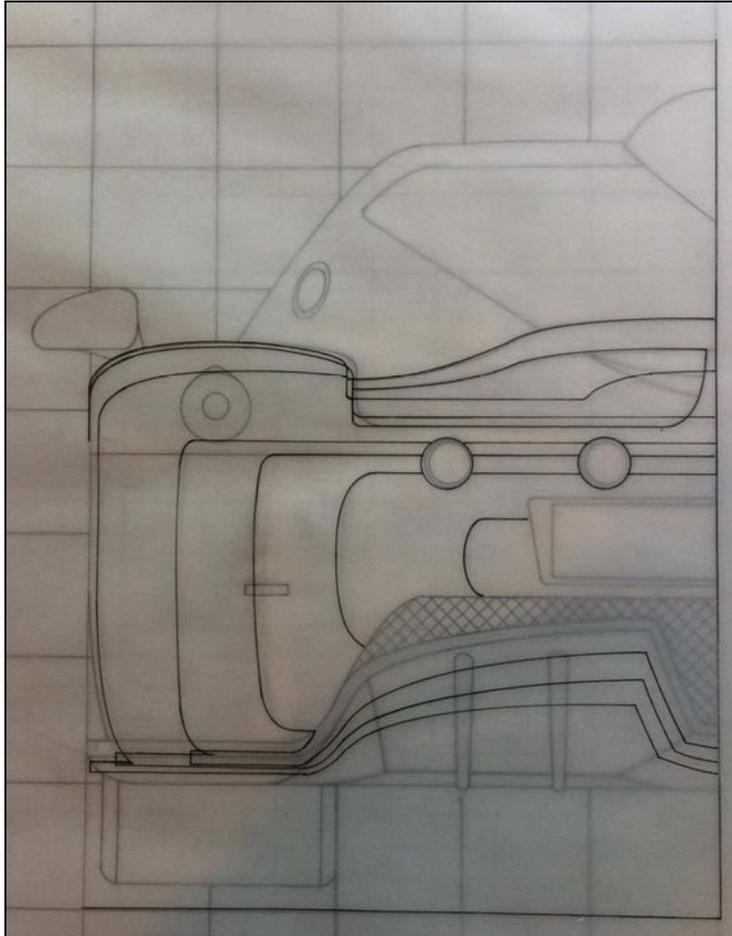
Sezione trasversale in loco (prospetto posteriore)
